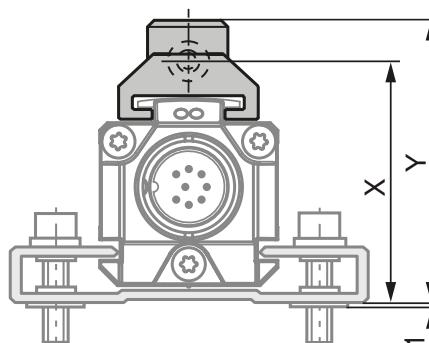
Dimensions et distances pour le capteur de position BTL5-M/N-2814-1S
